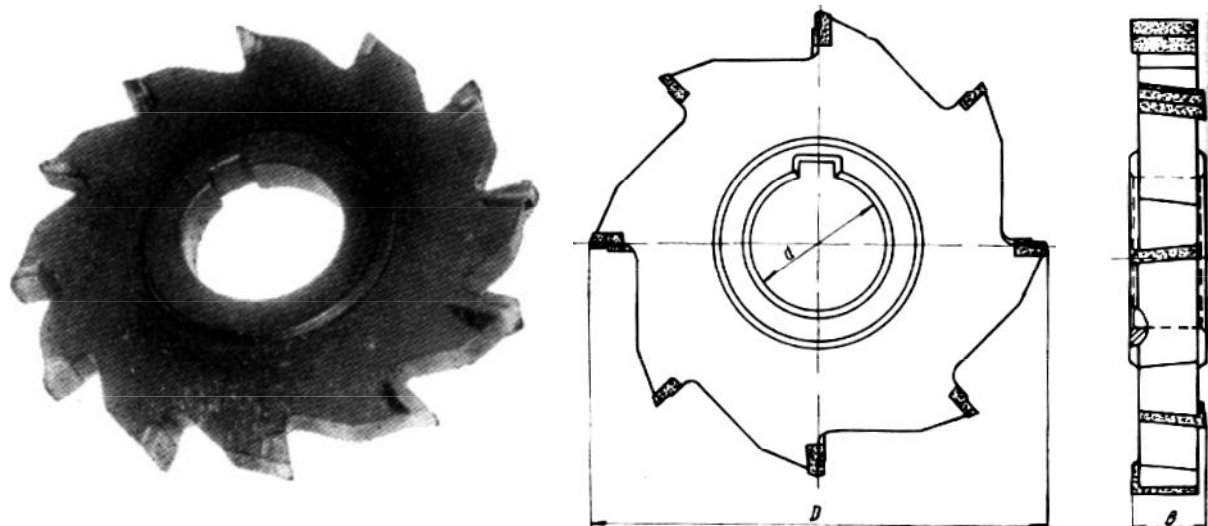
Дисковая фреза с напайными пластинами из быстрорежущей стали
